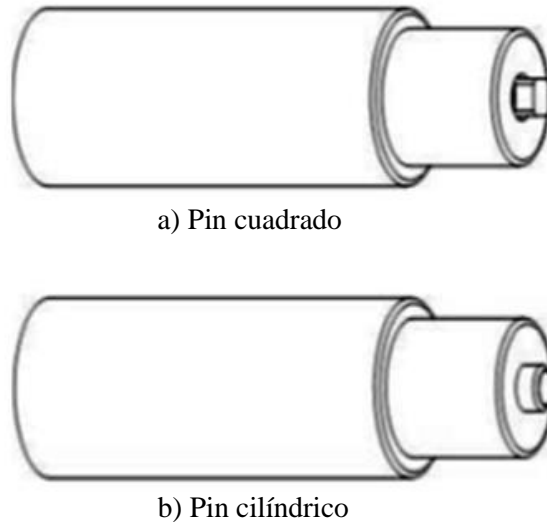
Herramienta de soldadura: a) Pin cuadrado y b) Pin cilíndrico
